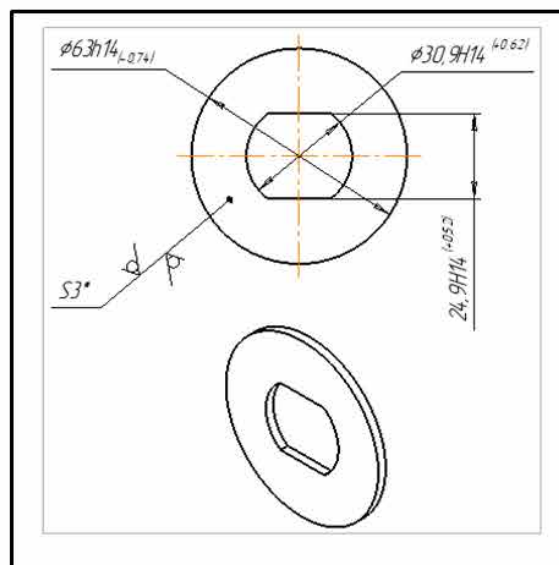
Ескіз кресленика деталі «Шайба»
